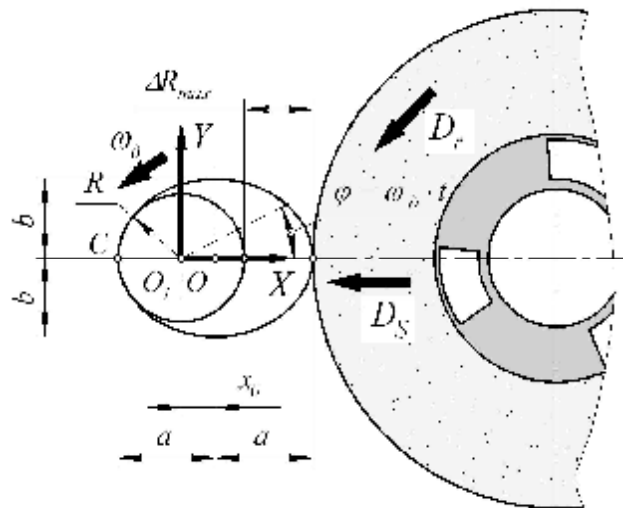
Шліфування заготовки з еліпсним перерізом
